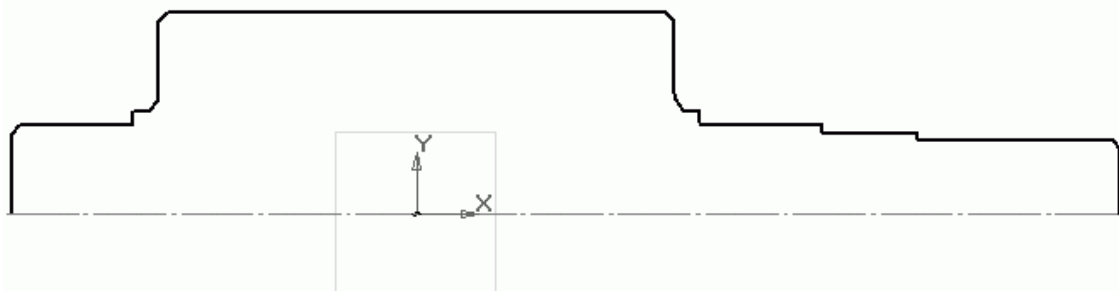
Эскиз контура ведущего вала-шестерни
